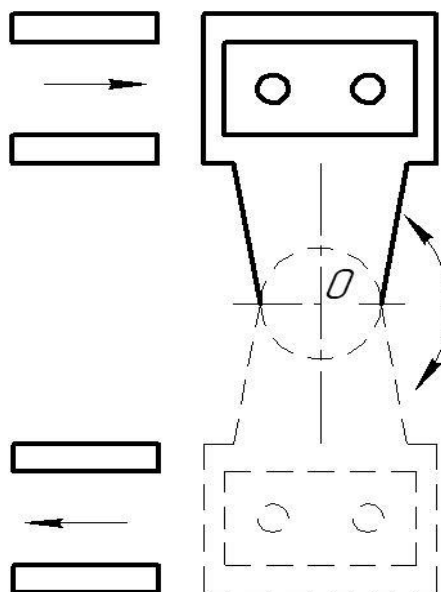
Схема спрацьовування поворотного столу з винесеним центром повороту
